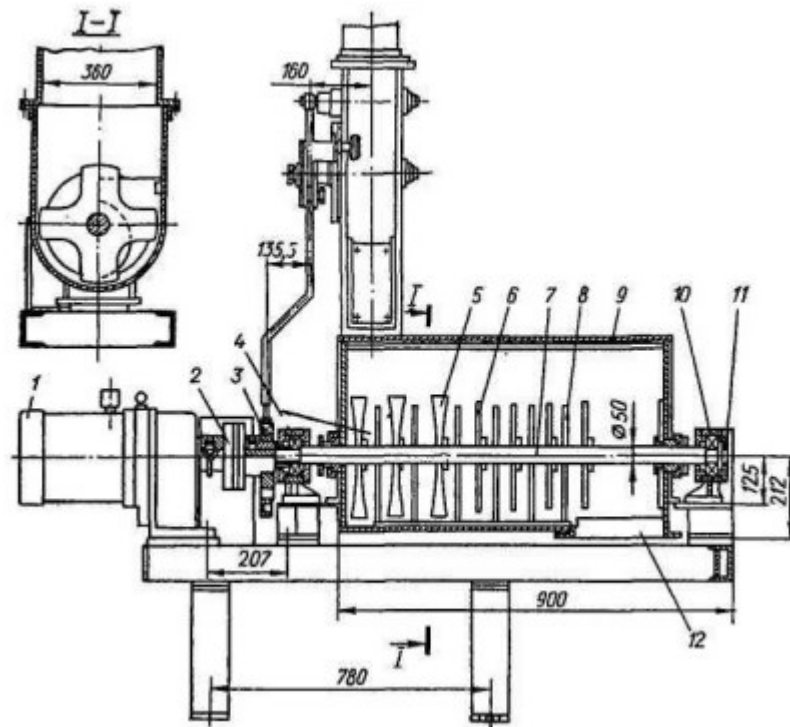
Тістомісильна машина А2-ХТТ: 1 - двигунредуктор; 2 - з'єднувач; 3 - ексцентрик; 4 - робоча камера; 5 - чотирилопатеві диски; 6 - плоскі диски; 7 - вал; 8 - гальмівні лопаті; 9 - кришка; 10 - підшипник; 11 - станина; 12 - розвантажувальний патрубок
